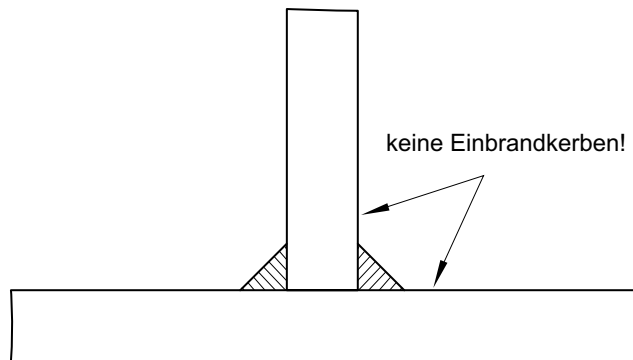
Schweißnahtausführung bei X- und Y-Naht ESC-003
